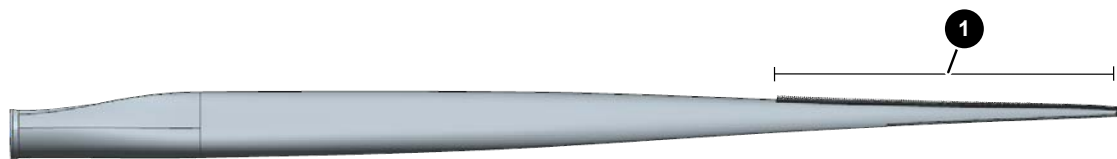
Position der Hinterkantenkammsegmente am Rotorblatt
